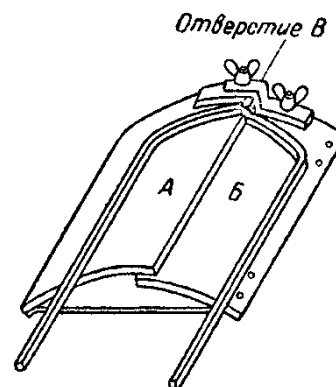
Приспособление для выгиба лобовой части по радиусу.
